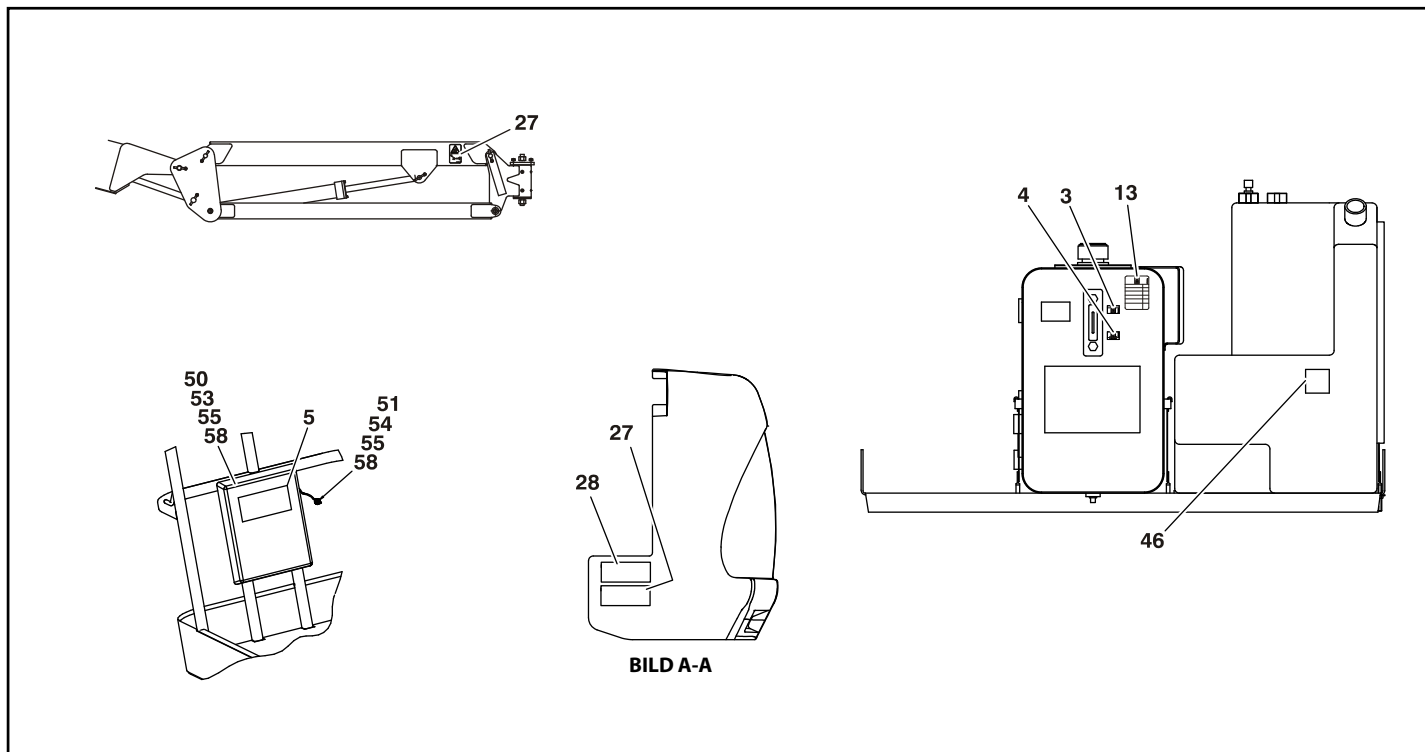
Placering av dekaler – Blad 3 av 4
